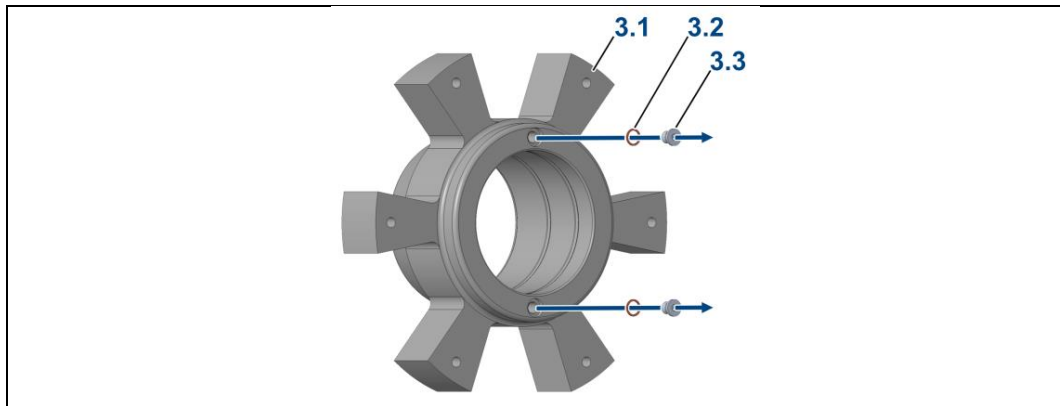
Verschlusschrauben lösen und entfernen (Beispiel) – 3.1 Achsstern, 3.2 Dichtring, 3.3 Verschlusschraube
